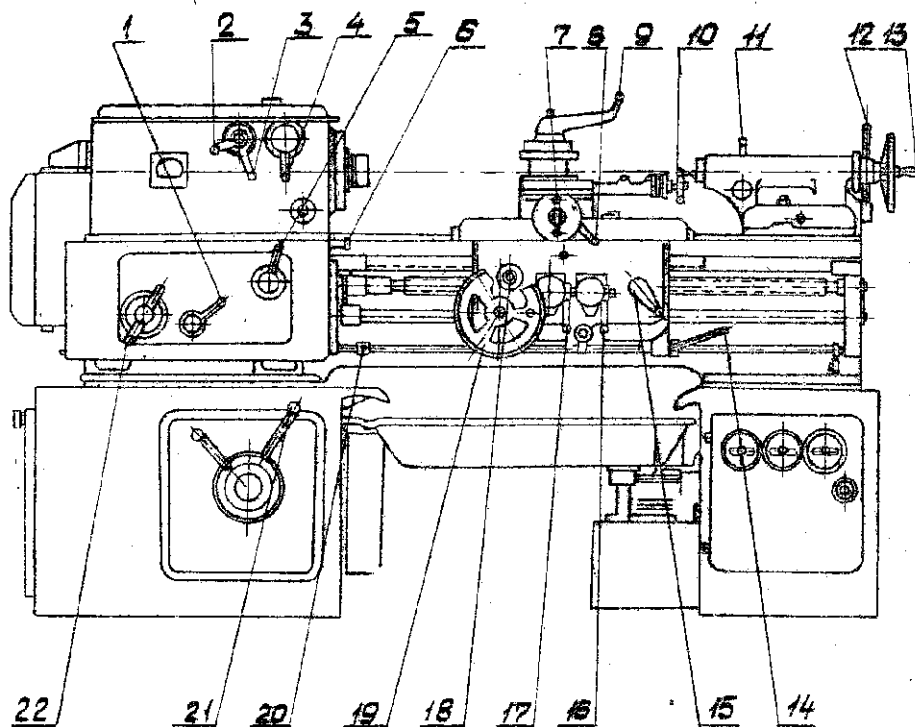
Токарно-винторезный станок IА6I6 (органы управления).
